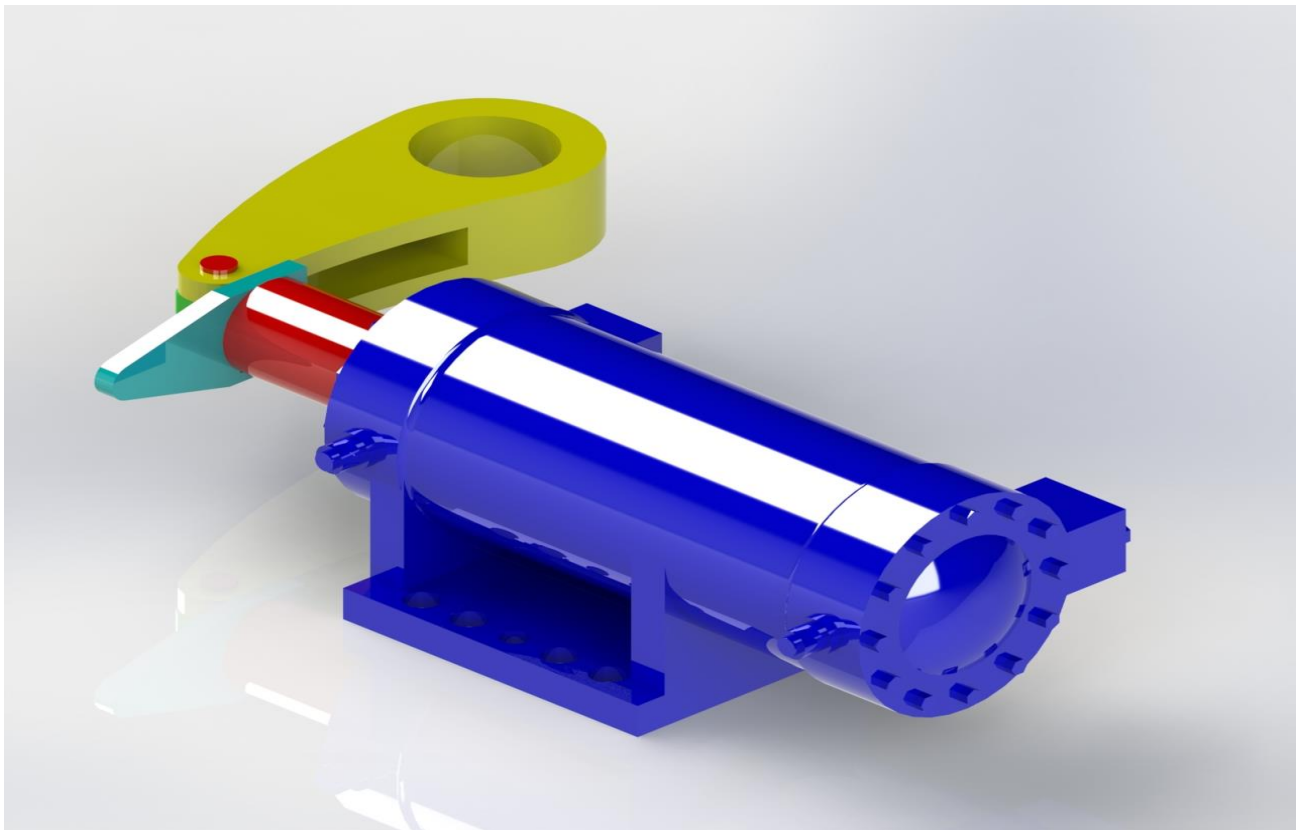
Cilindro actuador de doble efecto vista frontal derecha.
